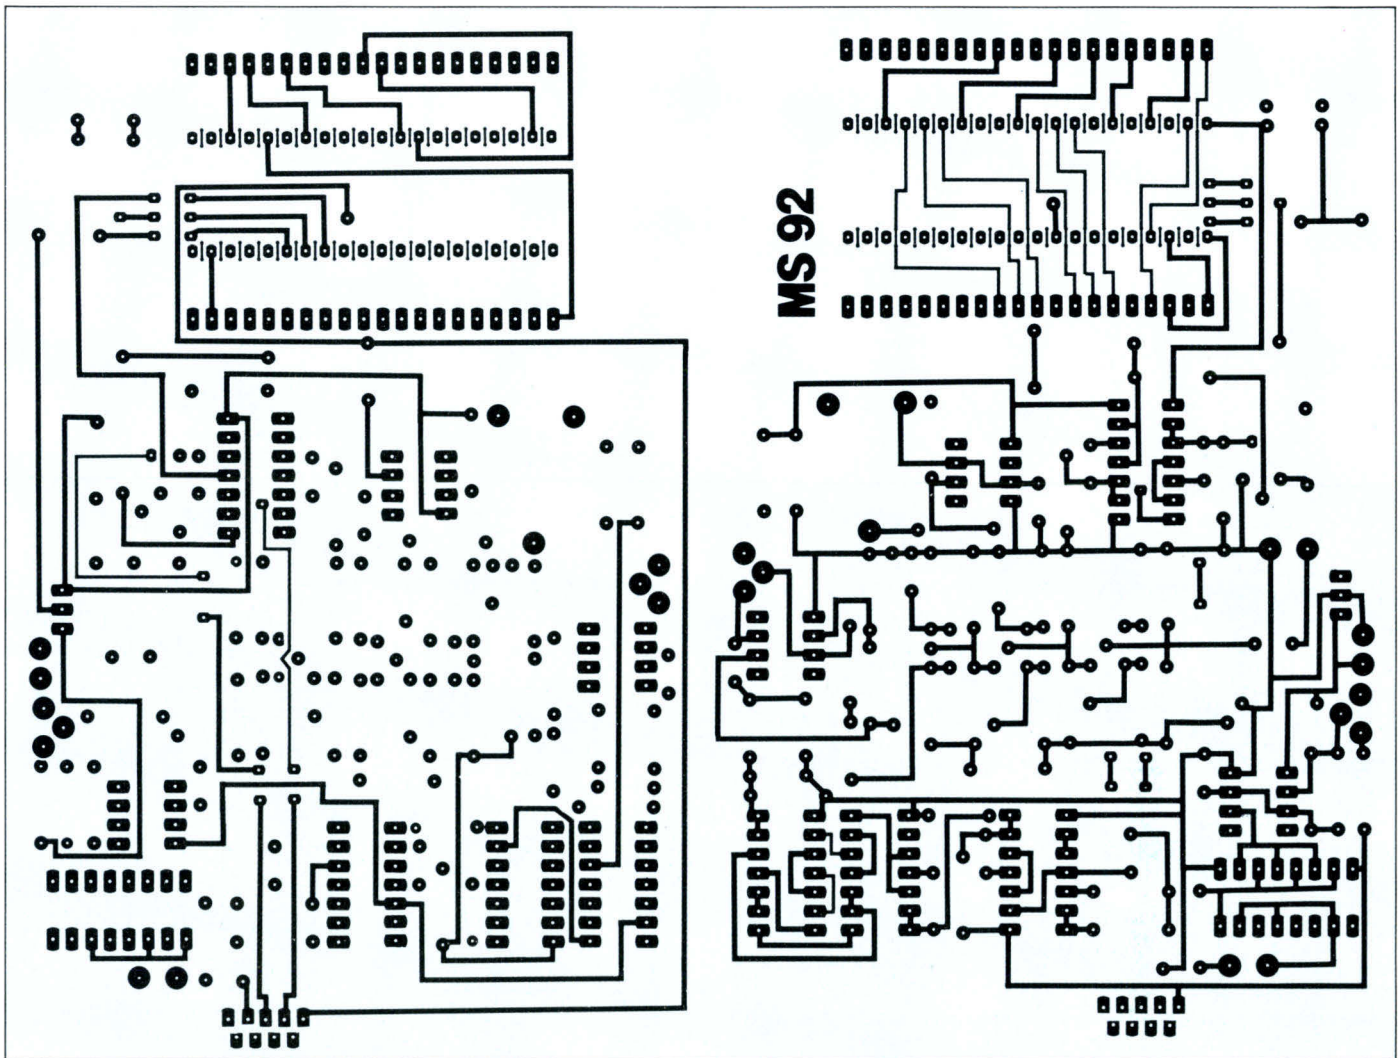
a) Circuit imprimé vu côté soudures. — b) Vu côté composants.
